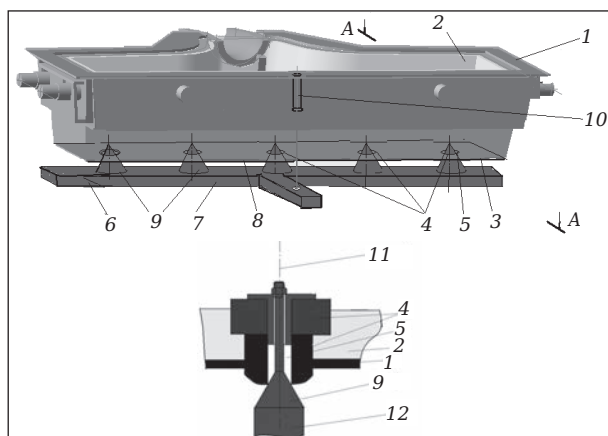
Установка на промежуточном ковше имитатора рабочей среды (а) и элемент имитатора (б)
